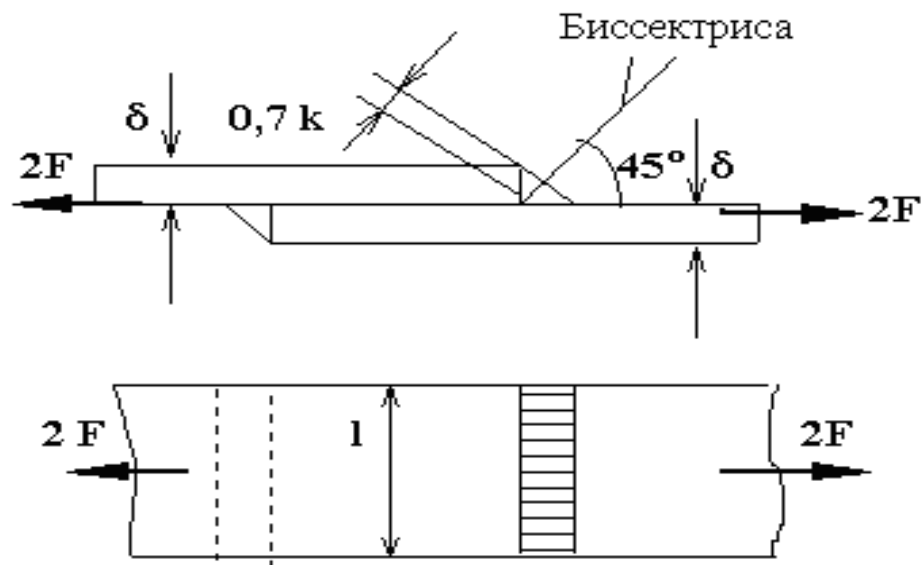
Схема расчета на срез по опасному сечению
